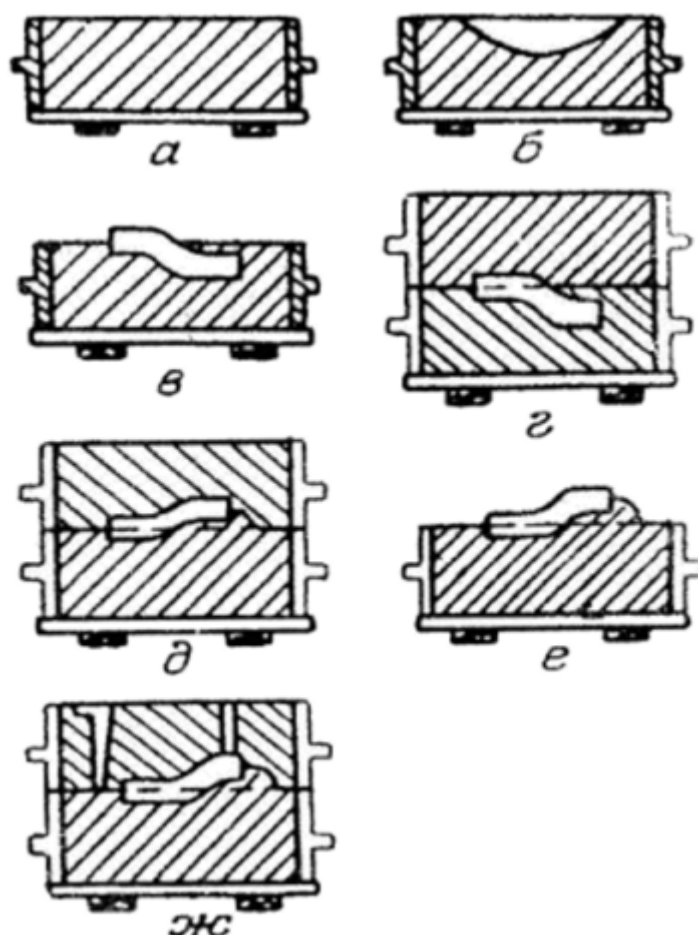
Формовка с подрезкой а — модель ; б- формовка нижней опоки ;
